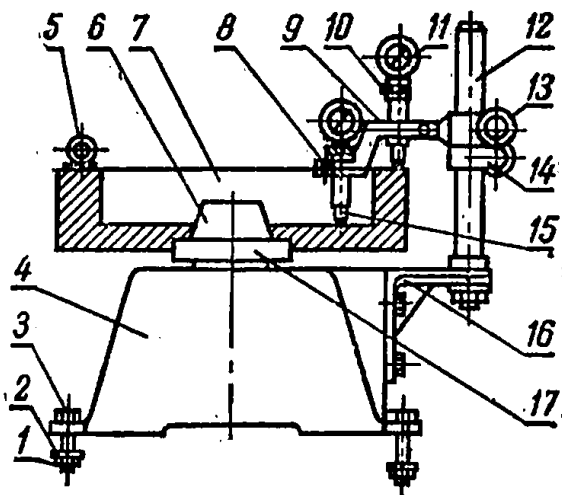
Приспособление для контроля маховика двигателя СМД-14:
